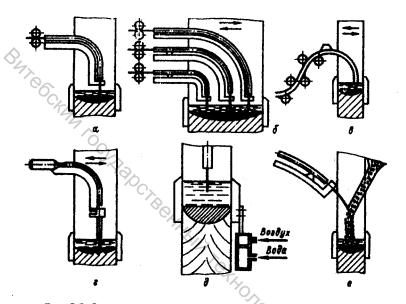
Электрошлаковая сварка проволочными электродами:
